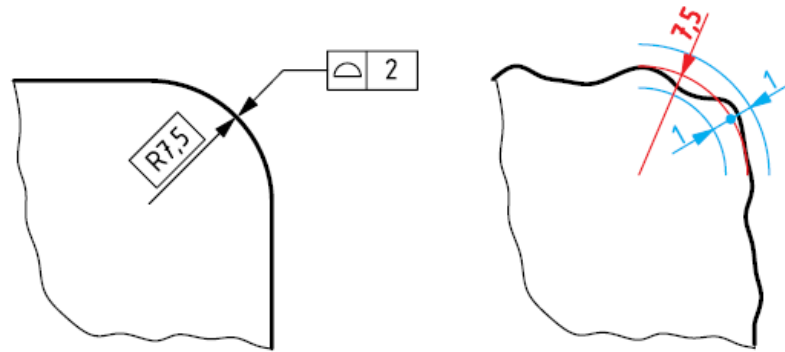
Radiustolerierung mit Profil einer beliebigen Fläche [Nie12]
